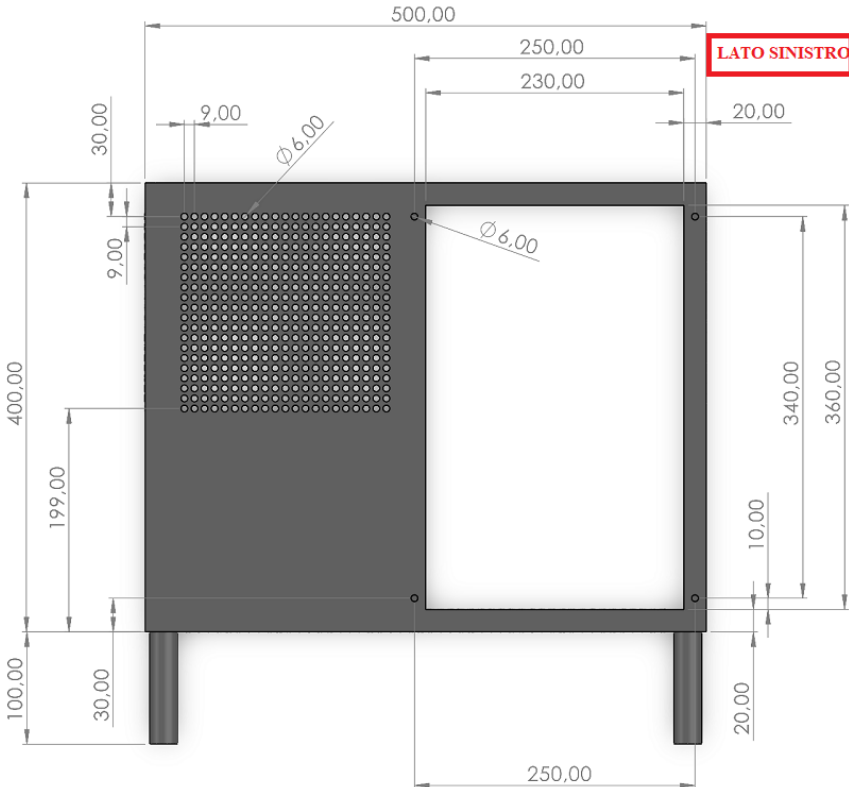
Lato sinistro della struttura a box con quote in millimetri
